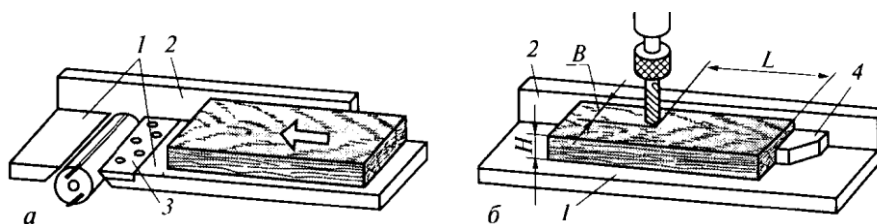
Базування деталі: *а* – рухоме; *б* – нерухоме; 1 – столи; 2 – напрямна лінійка; 3 – накладка; 4 – упор
